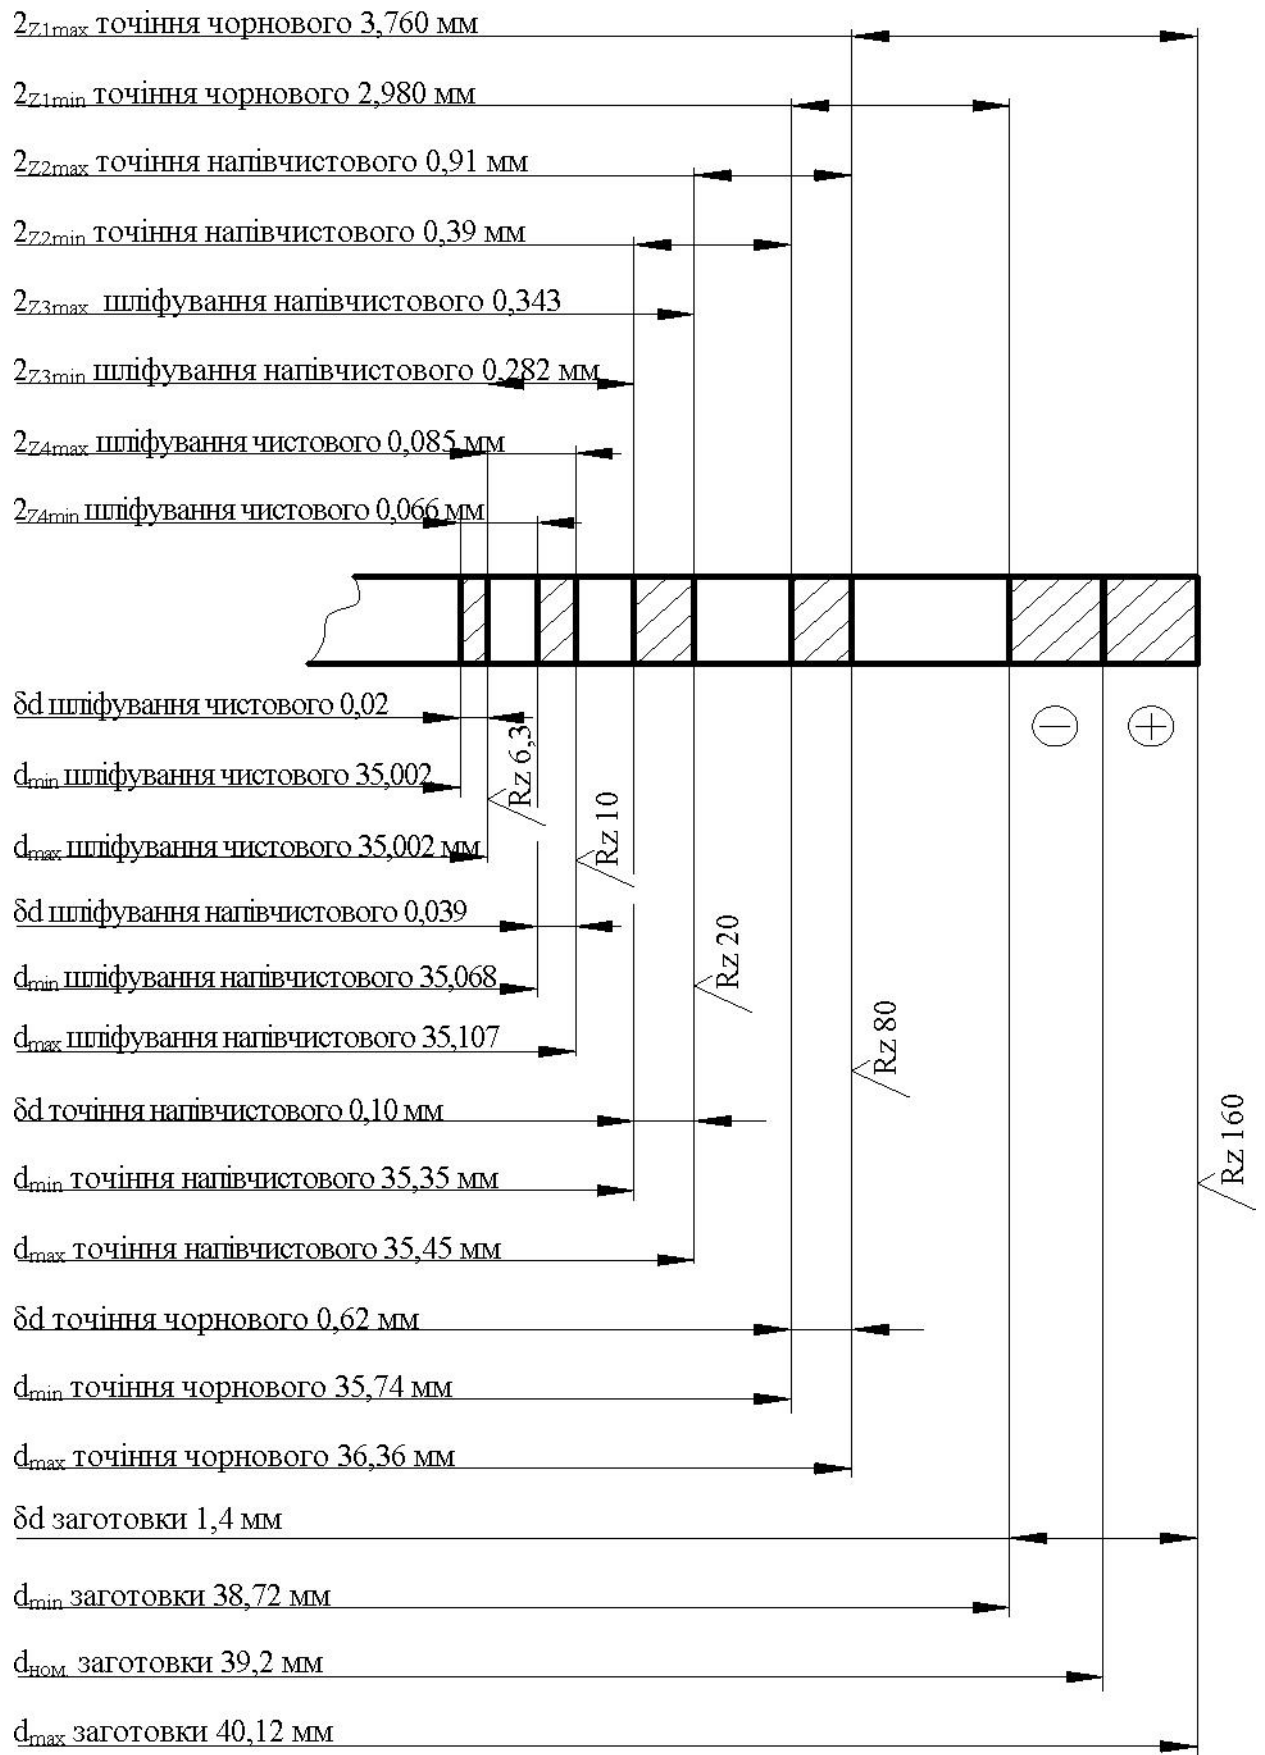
Схема графічного розташування припусків та допусків на обробку поверхні $\varnothing 35k6$
